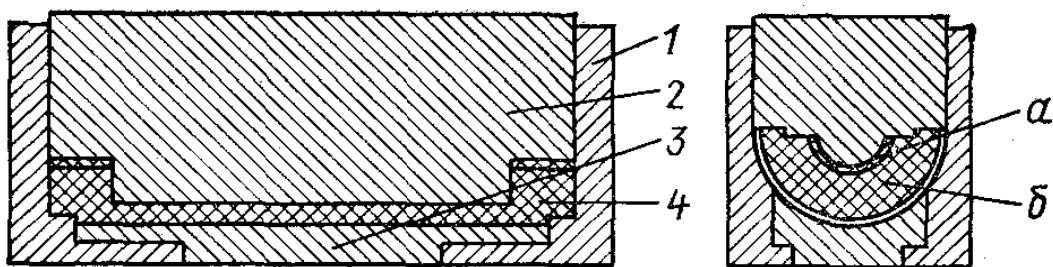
Схема формирования ролика ленточного конвейера из АМДП и древесного шпона:
